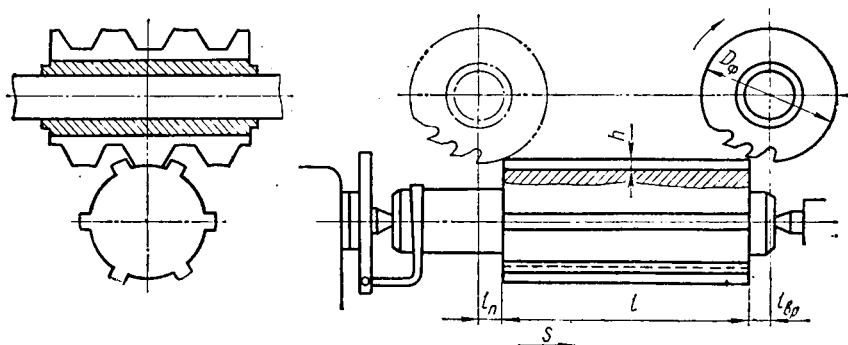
Схема фрезерования шлицев валов шлицевой червячной фрезой
